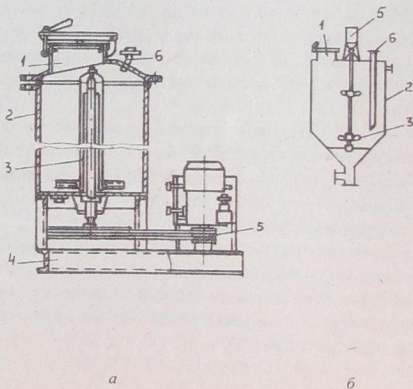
Краскосмесители с нижним (а) и верхним (б) расположением привода: 1 – загрузочный люк; 2 – корпус; 3 – мешалка; 4 – рата; 5 – привод мешалки; 6 – патрубок
